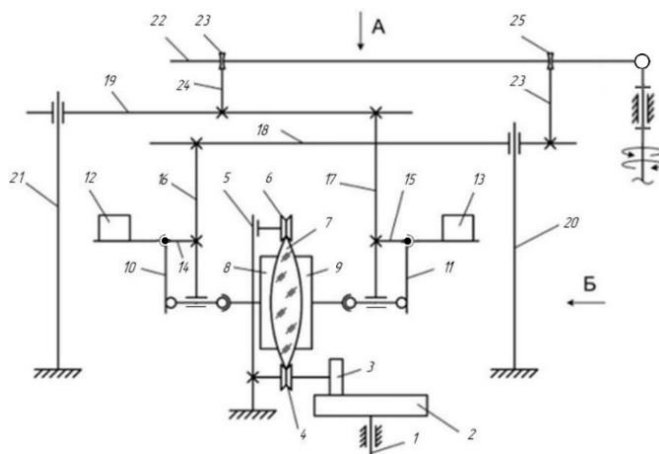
Кинематическая схема устройства для двусторонней обработки линз
